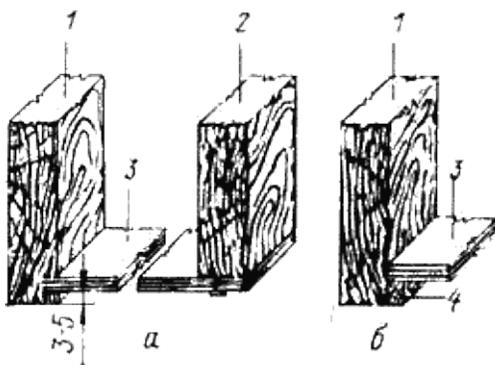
Крепление дна ящика к стенкам: а — с отборкой пазов; б —
